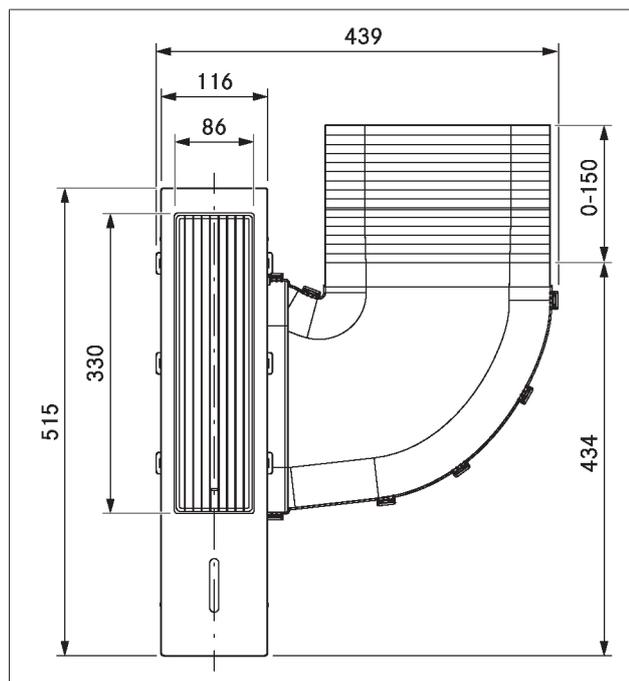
Dimensions CKA2/CKA2AB - Vue de dessus
